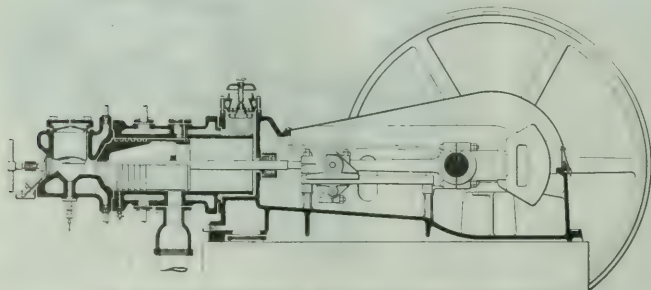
MOTOR BESSEMER CON REGULADOR DE MERCURIO
